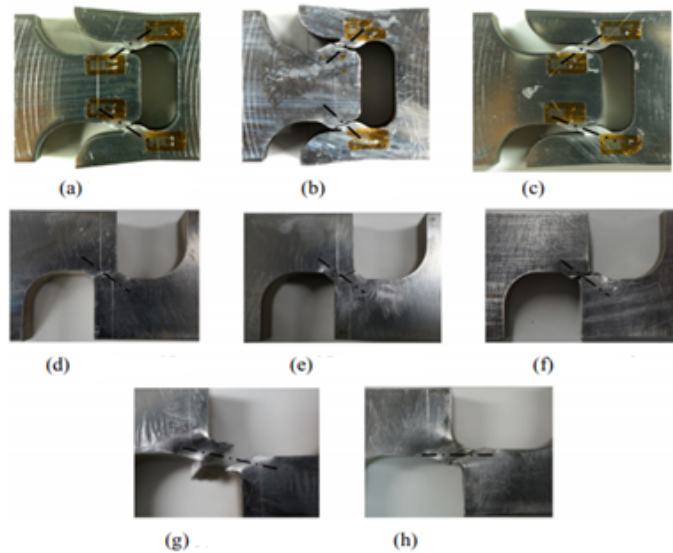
Figuras Macroscópicas de los ocho especímenes donde, a) probeta original, b) fractura en el transverso de la probeta, c) fractura en la unión, d) unión soldada antes de las pruebas de tensión, e) fractura en transverso de la unión, f) deformación en el cordón, g) resultado de la tensión, h) endurecimiento por deformación [4]
